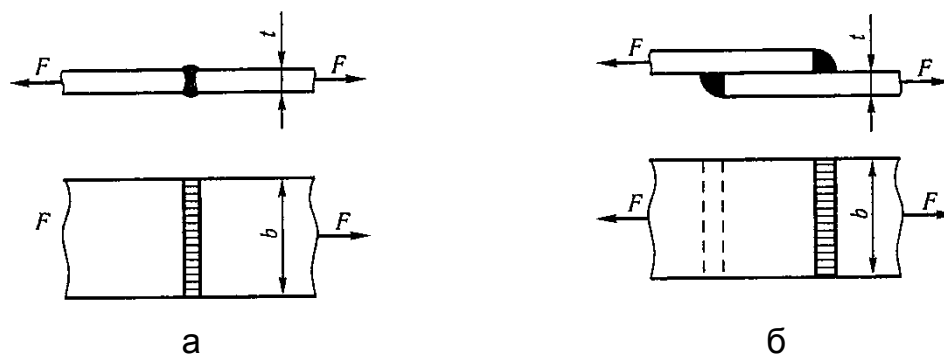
Схема до розрахунку зварного з'єднання:
